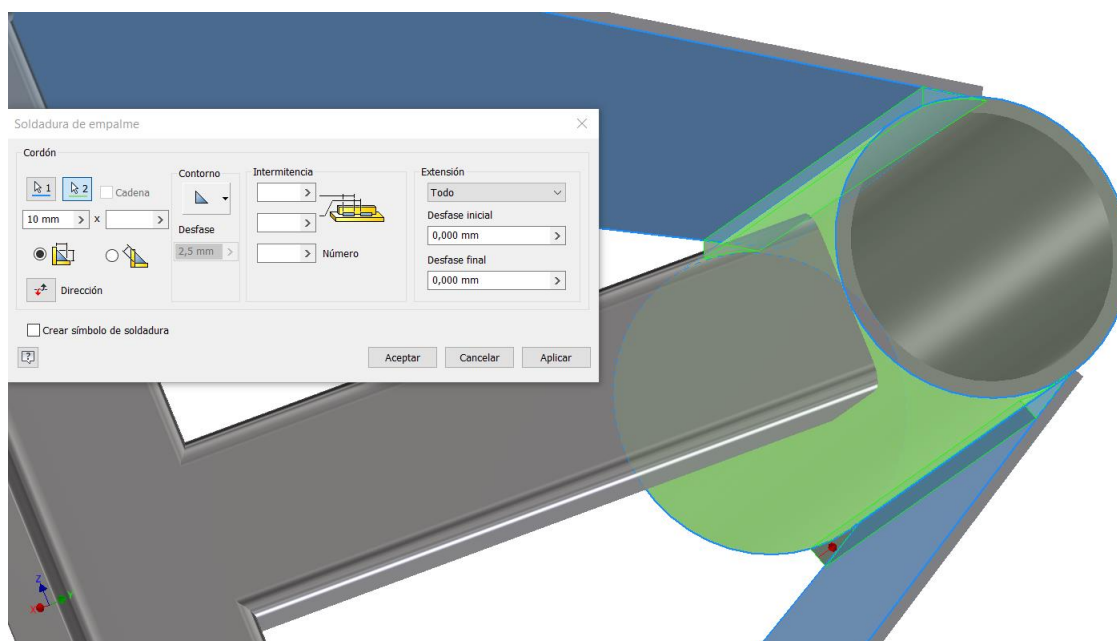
Soldadura de la placa de refuerzo con el tubo de dirección.
